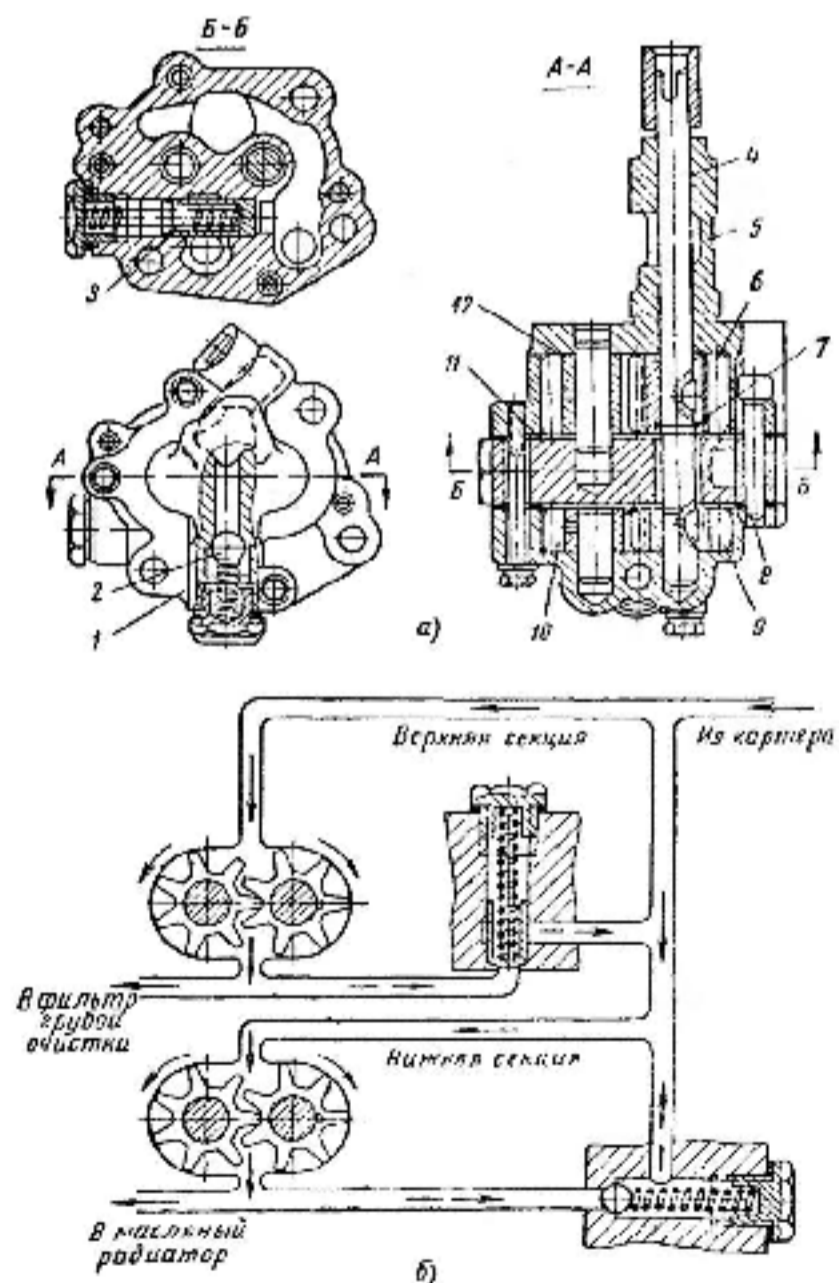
Устройство двухсекционного масляного насоса: а -устройство; б - схема работы; 1-корпус нижней секции,2 и 3-редукционные клапана,4-вал насоса,5-корпус верхней секции,6 и 9-ведущие шестерни,7-стопорное кольцо,8-штифт,10 и 12-ведомые шестерни,11-крышка
